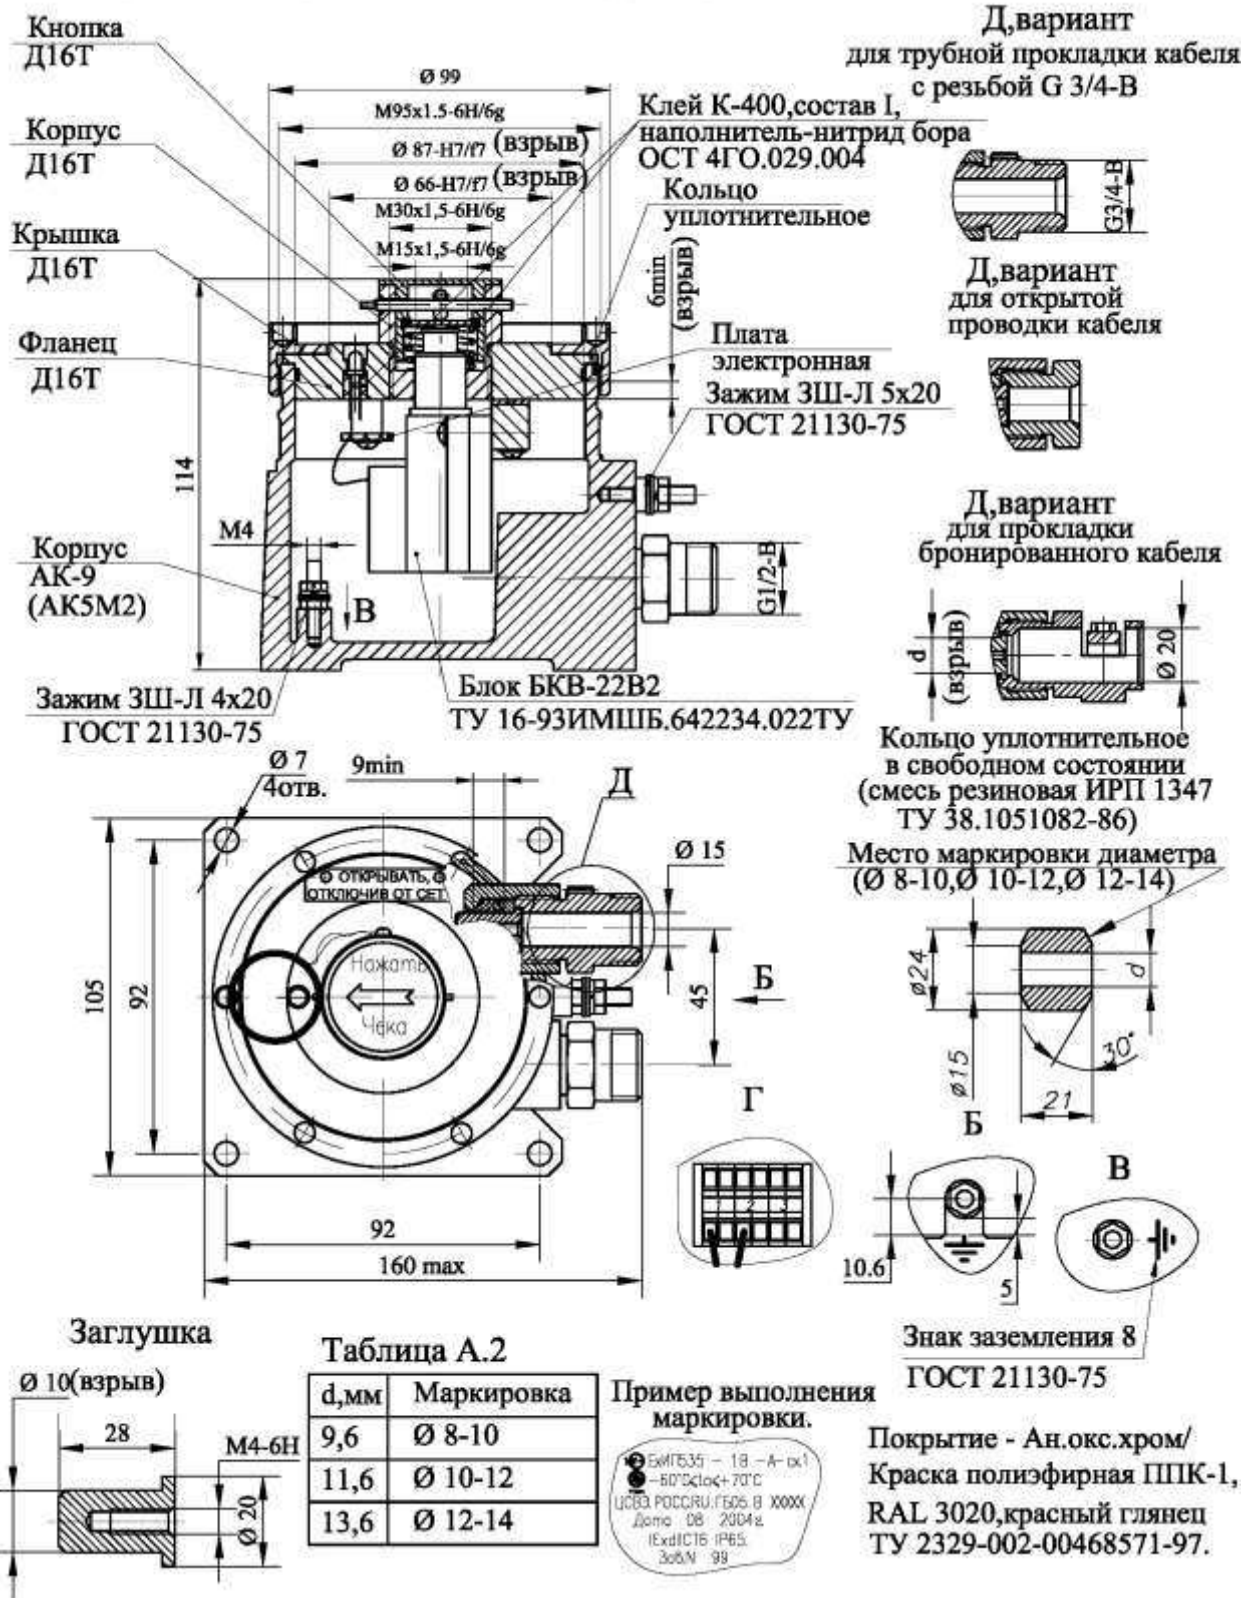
Габаритный чертеж извещателя Ех ИП535-1В в алюминиевом корпусе, совмещённый с чертежом взрывозащиты
